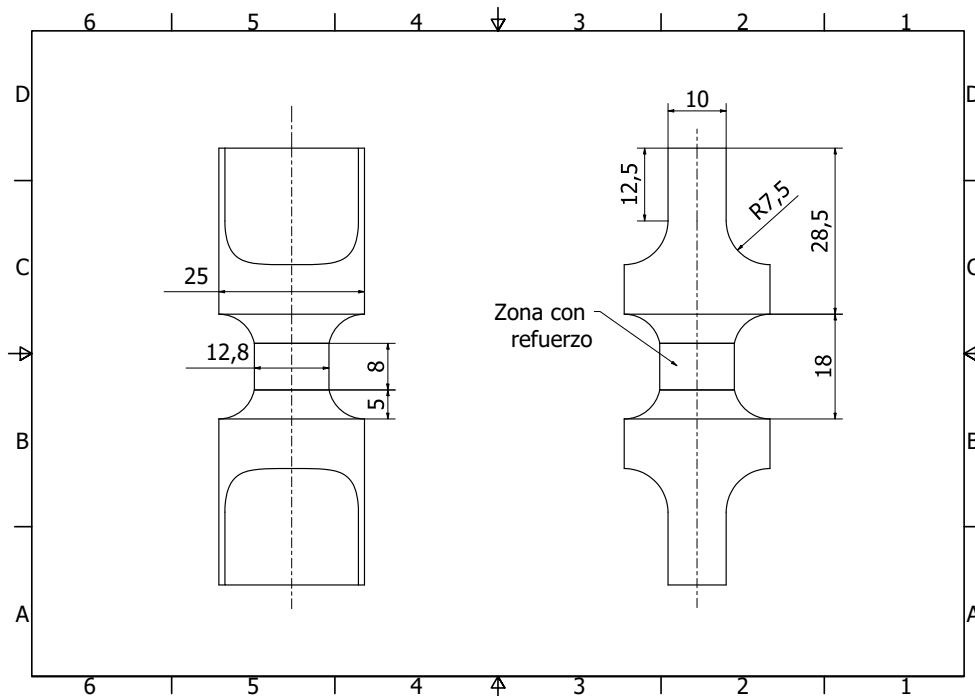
Geometría utilizada en los ensayos de tracción fuera del plano
